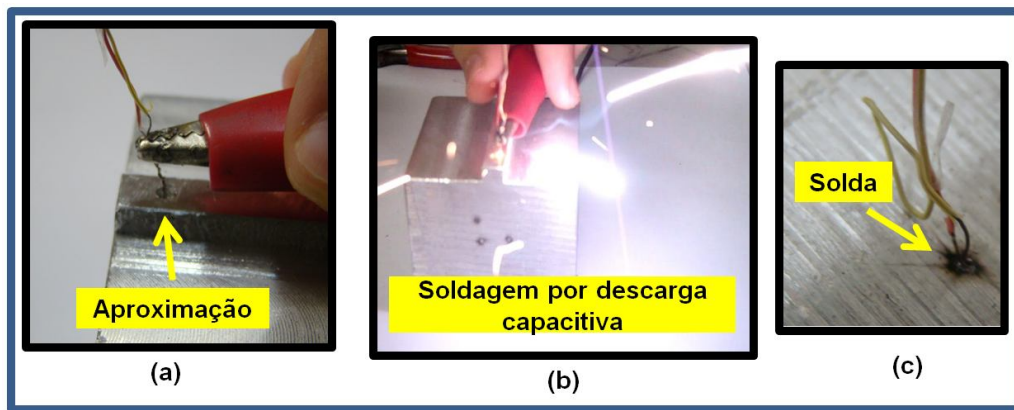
Sequência de soldagem: (a) – Aproximação do termopar na peça, (b) – Procedimento de soldagem por descarga capacitiva e (c) – Resultado da solda do termopar na peça.
